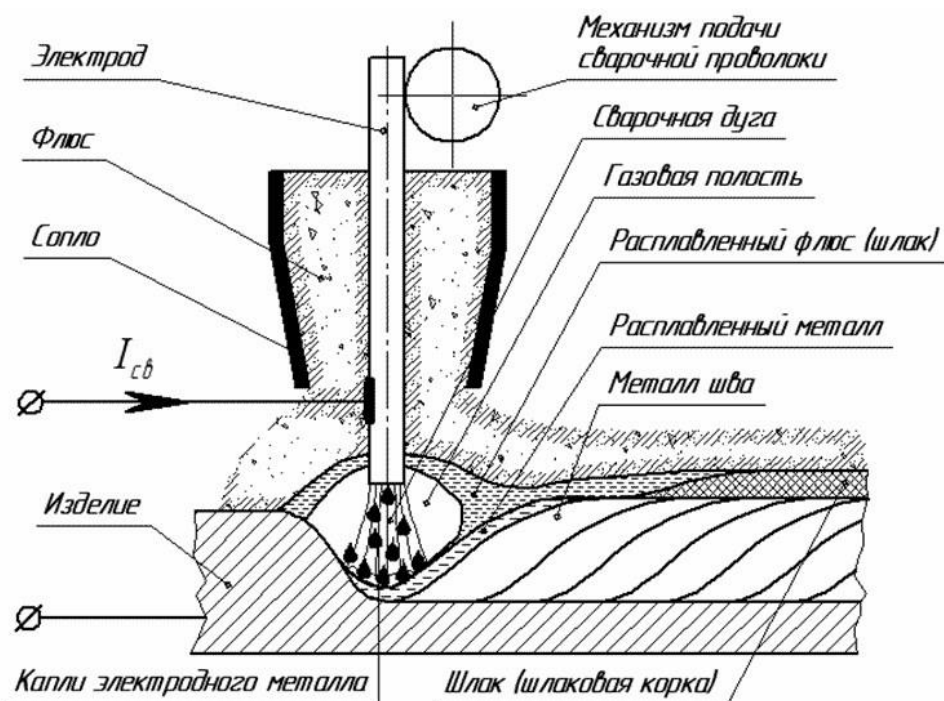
Схема процесса автоматической дуговой сварки под флюсом
